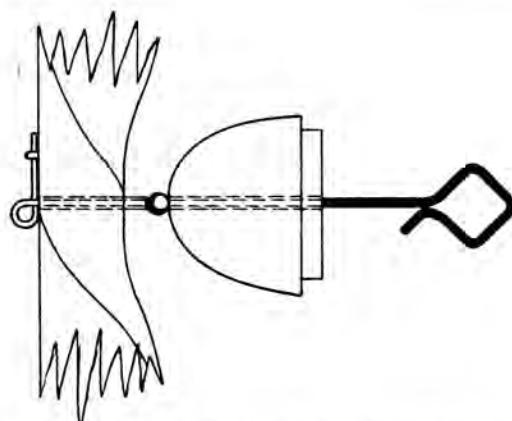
Zweckmäßige Ausführung der Luftschraubenwelle.
